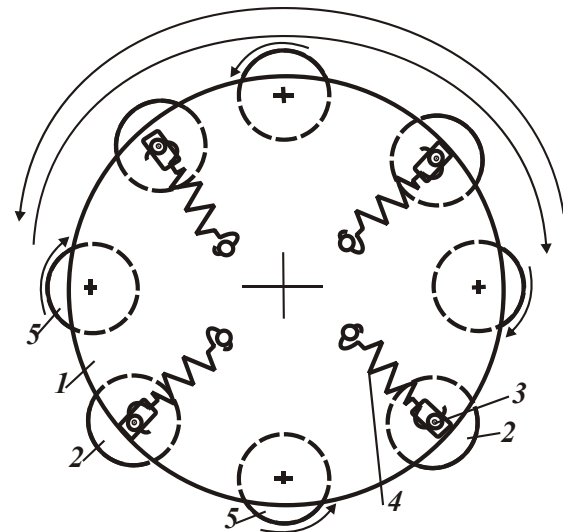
Инструмент для совместной обкатки и шлифования: 1 - корпус; 2 - обкаточные круги; 3 - оси обкаточных кругов; 4 - пружины обкаточных кругов; 5 - шлифовальные круги.
